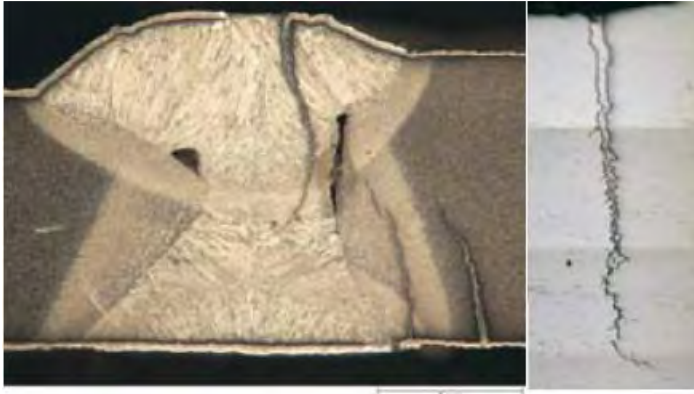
Mit Zink gefüllte Risse in Schweißgut, WEZ und Grundwerkstoff eines Stumpfstoßes [Lit 36]
